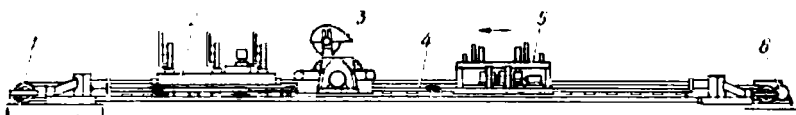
Общий вид круглопильного станка модели ЦДТ-7:
